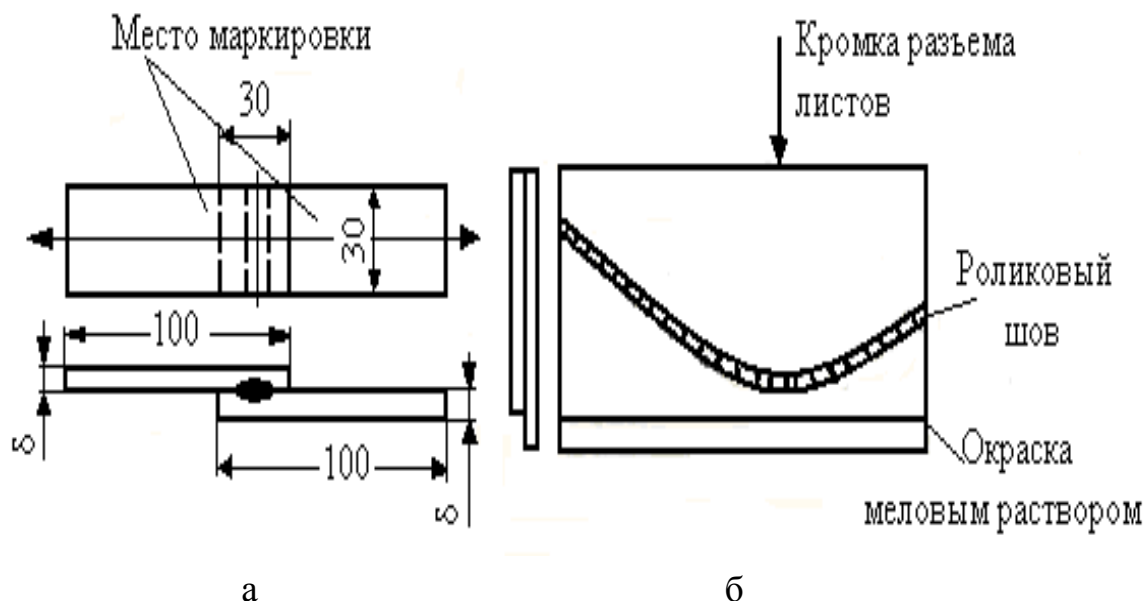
Образцы для испытания шовной сварки
